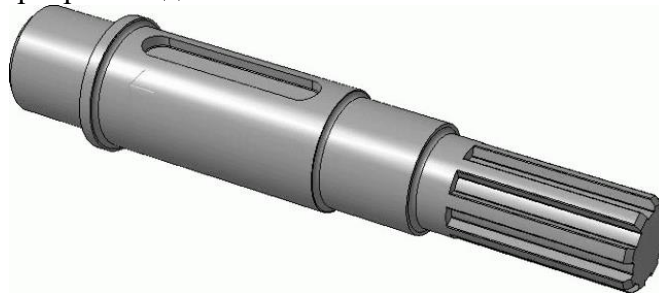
3D-модель детали «Шлицевой вал»
